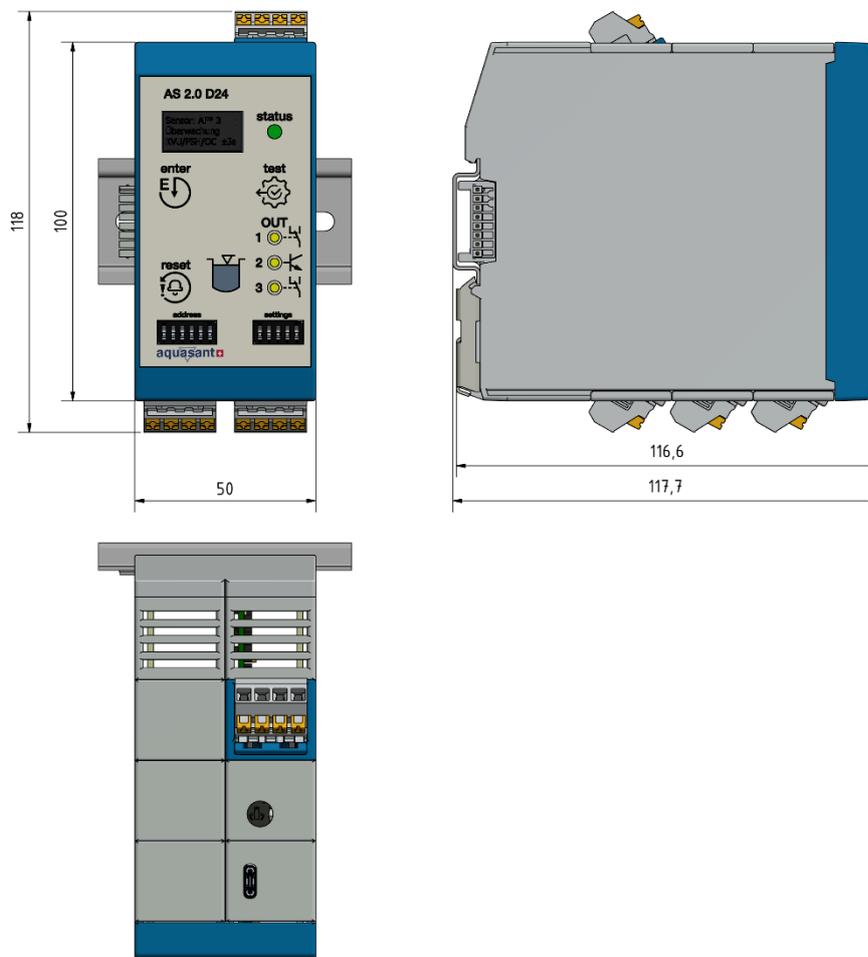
Gerätedimensionen, Auf-, Seitenansicht
